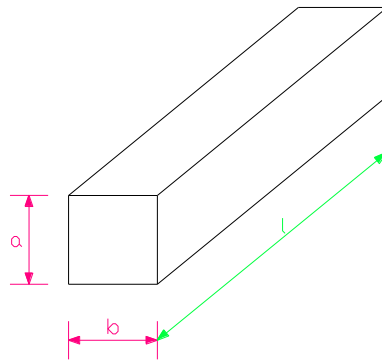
Dimensiones de la lengüeta. (Fuente: Propia)
